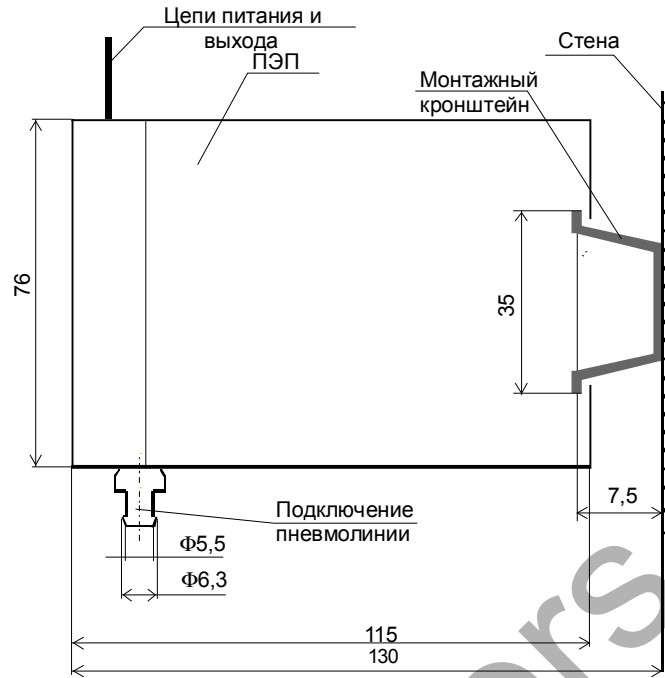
Габаритные и присоединительные размеры ПЭП
